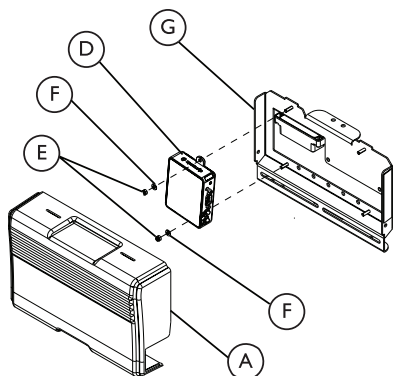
Remplacement du module d'entrée — Dossier manuel
